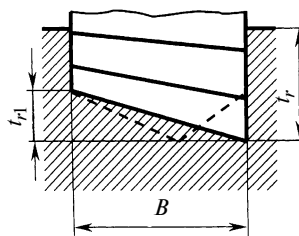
Параметры резания угловой фрезой, образующей паза с вертикальными стенками: штриховая линия — возможный вариант формы дна паза
